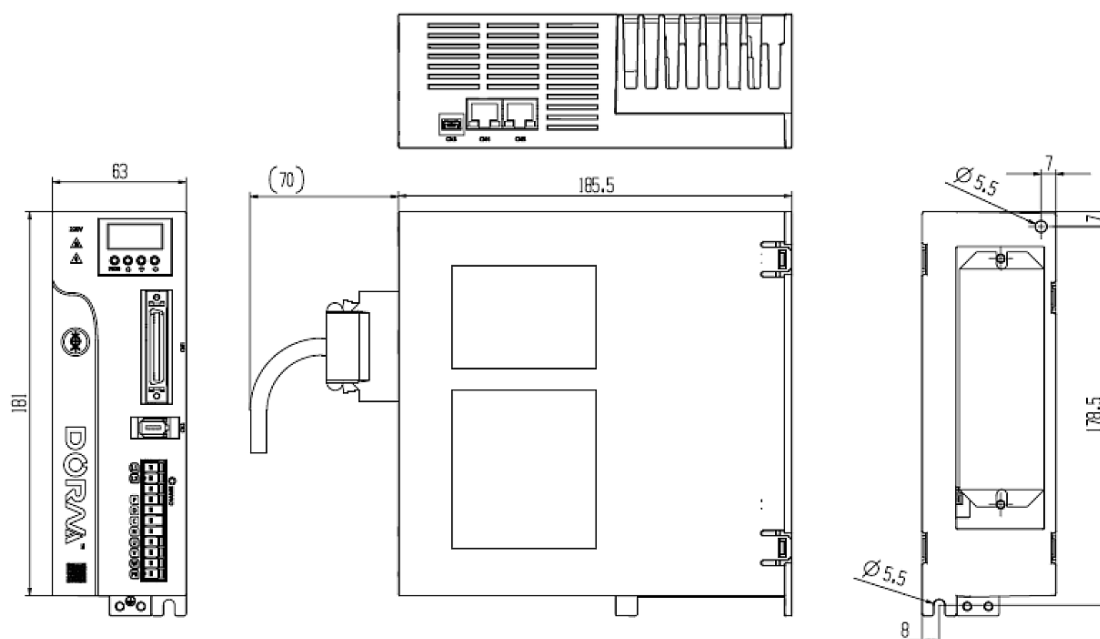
Габаритные размеры драйвера, тип корпуса В (220 В,  $\leq 2$  кВт)
